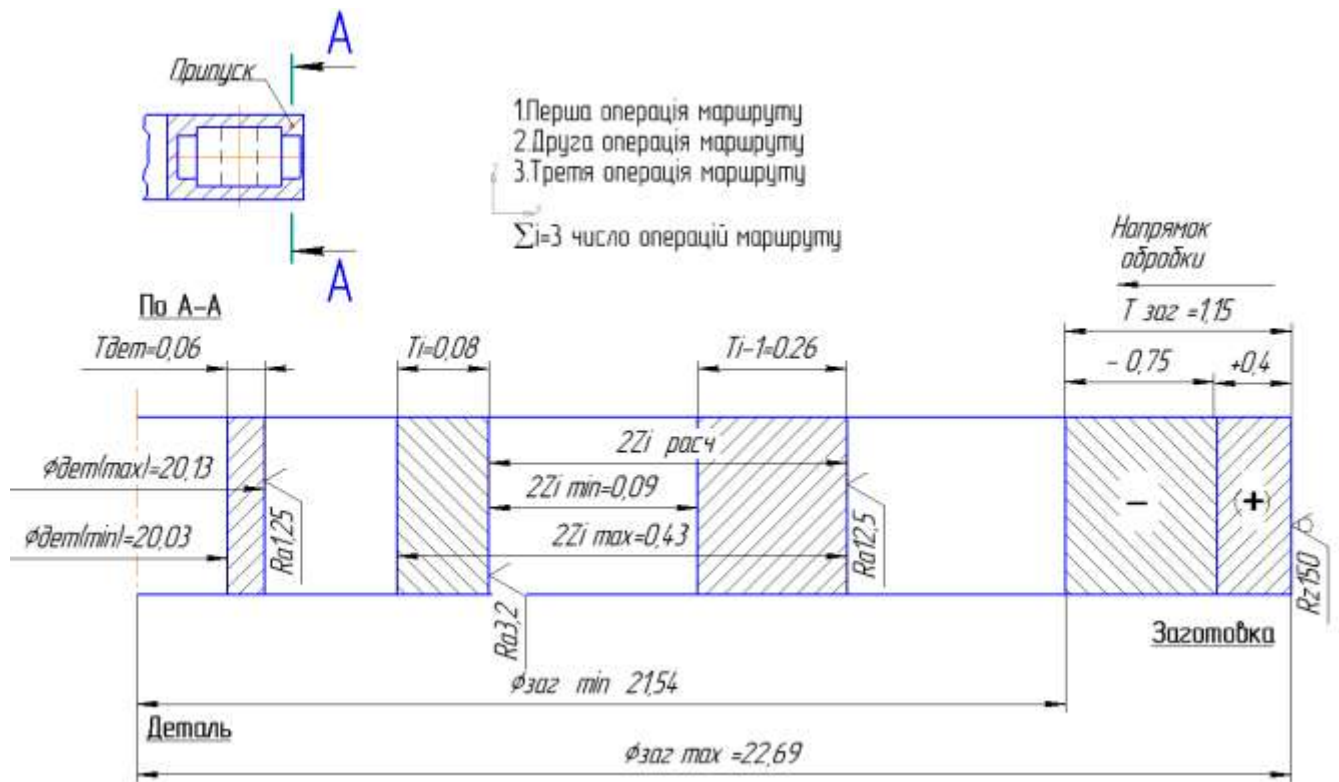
Схема графічного розташування припусків і допусків при обробці шийки шарніра $\varnothing 20h8$ мм
